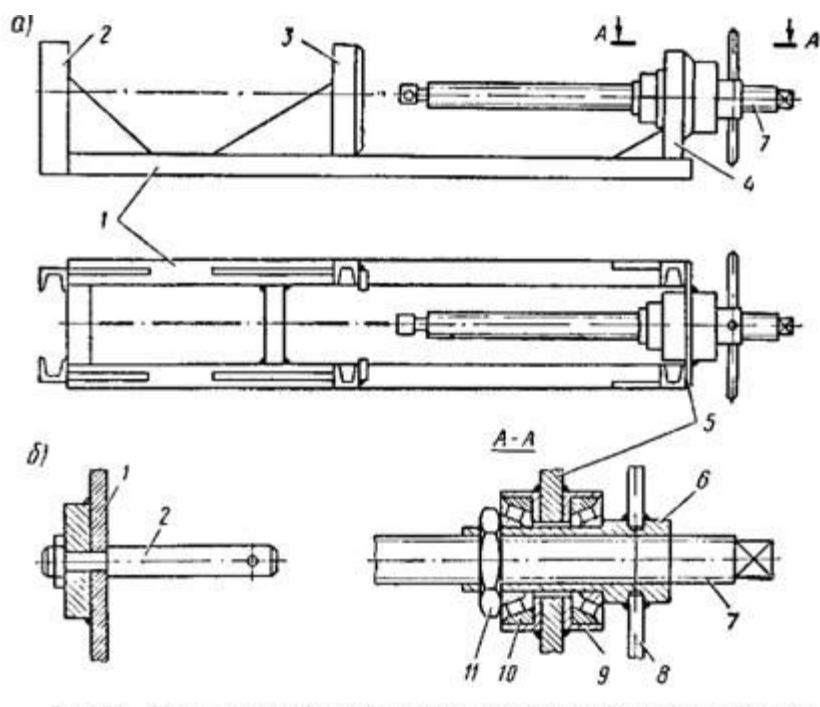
Стенд для разборки–сборки телескопического подъемника
